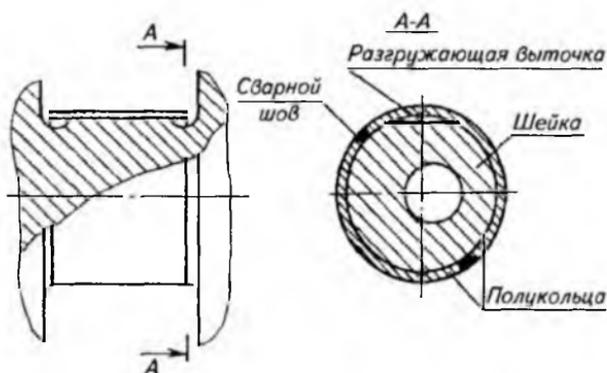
Схема восстановления шеек коленчатого вала двигателя ЗМЗ-53 приваркой стальных полуколец
